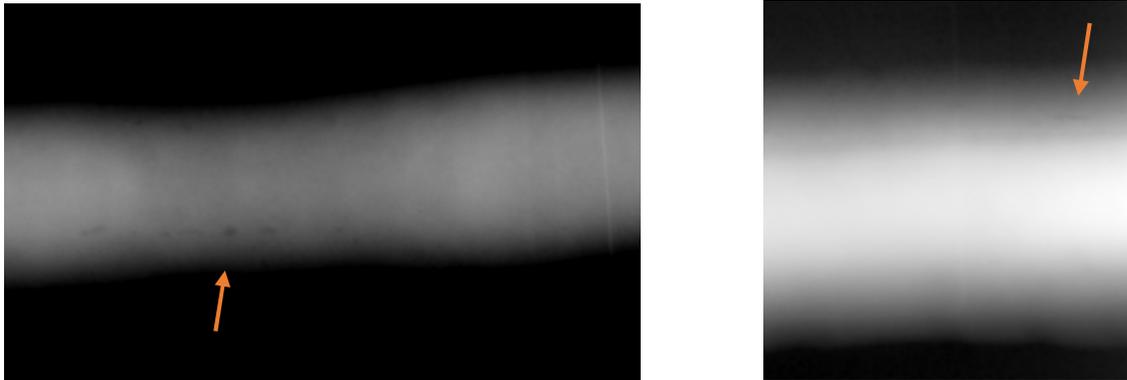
Autres zones de la soudure vue aux rayons X : à gauche inclusions alignées, à droite manque de fusion. Le recadrage des niveaux de gris est spécifique à chaque défaut.
